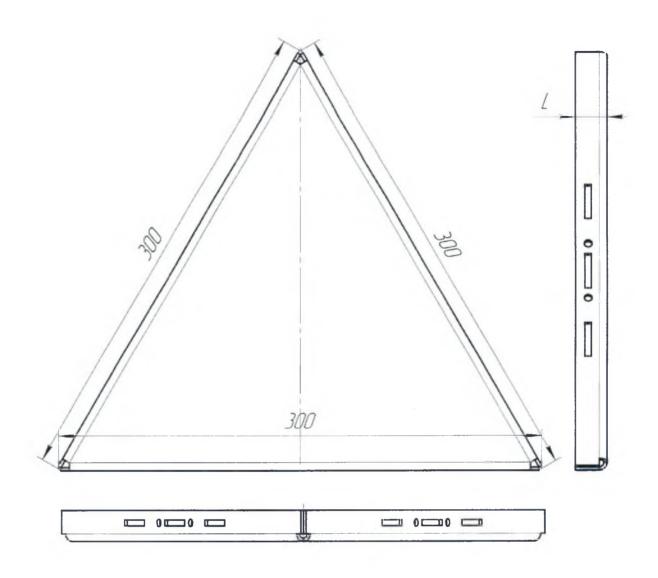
Пример конструкции треугольного информационного знака с универсальными отверстиями для крепления
